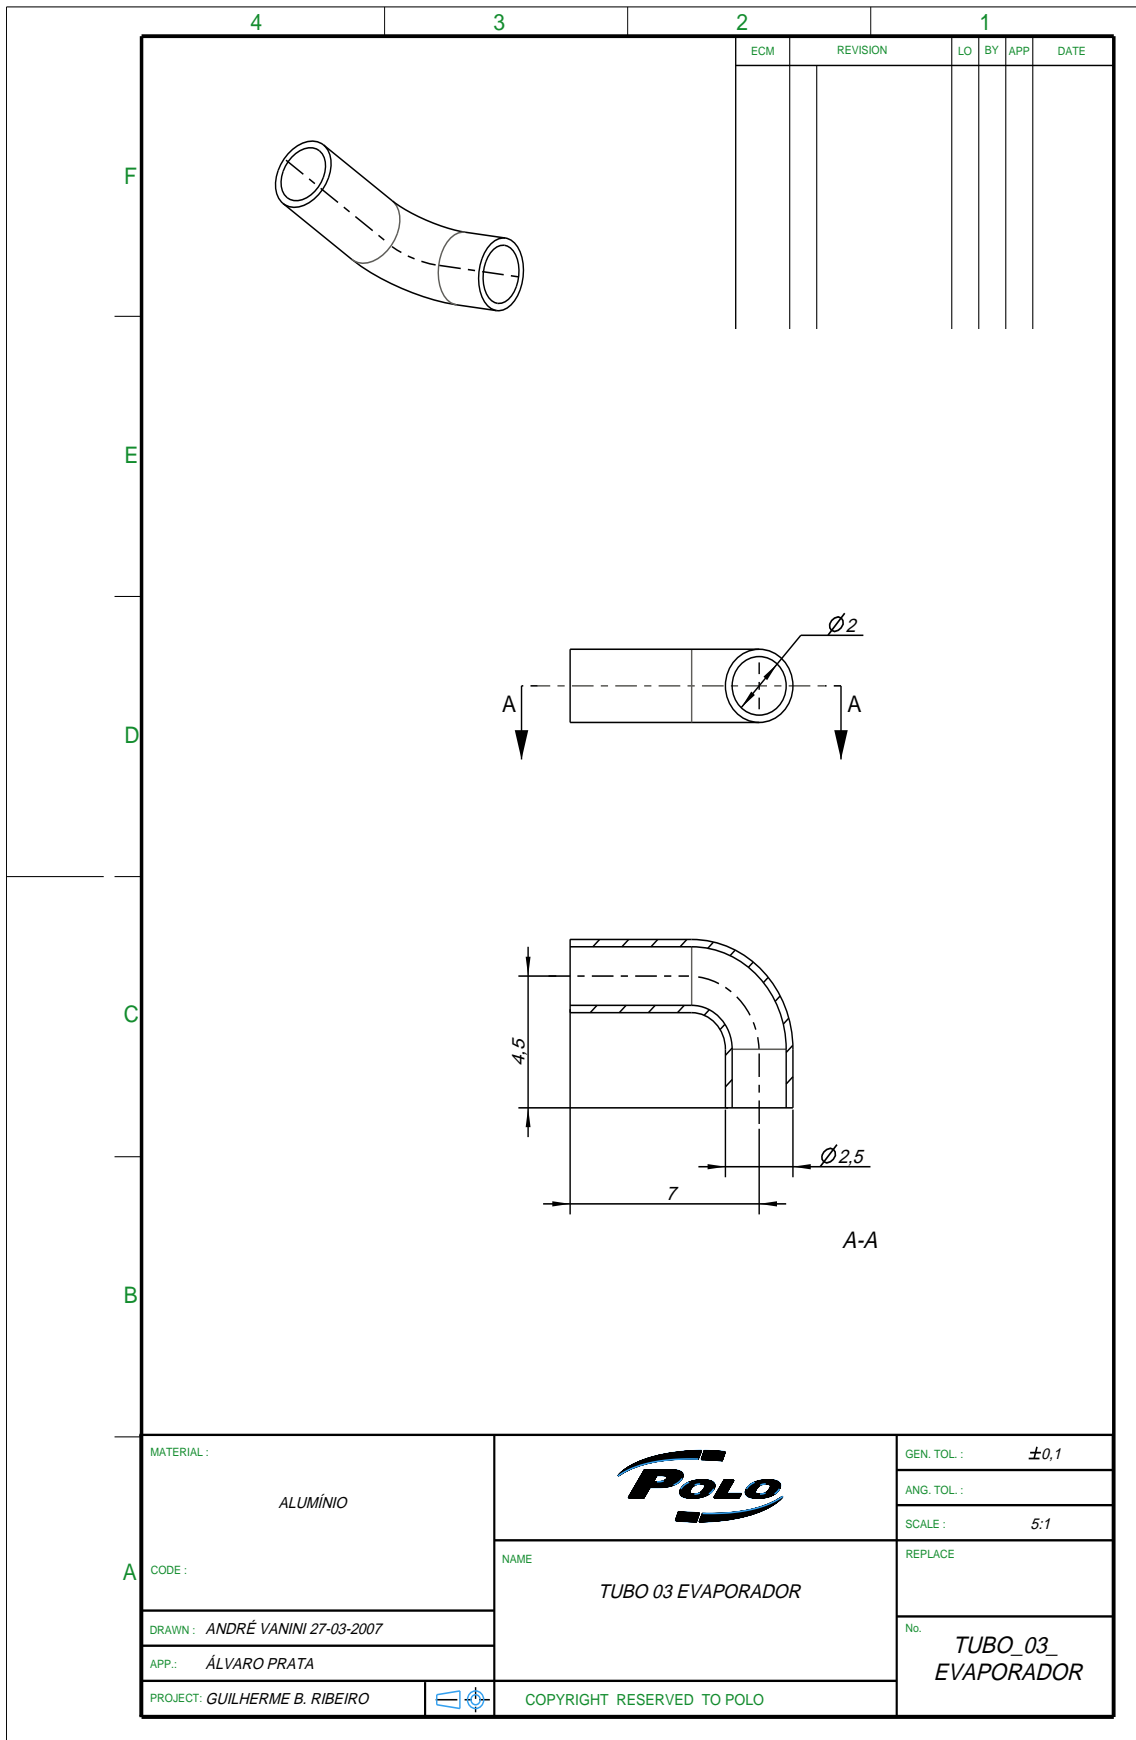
Desenho técnico do evaporador acoplado a tubos de calor - Parte VIII
